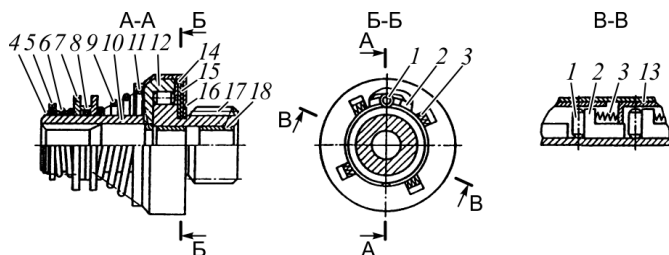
Механизм привода стартера с роликовой муфтой свободного хода:
